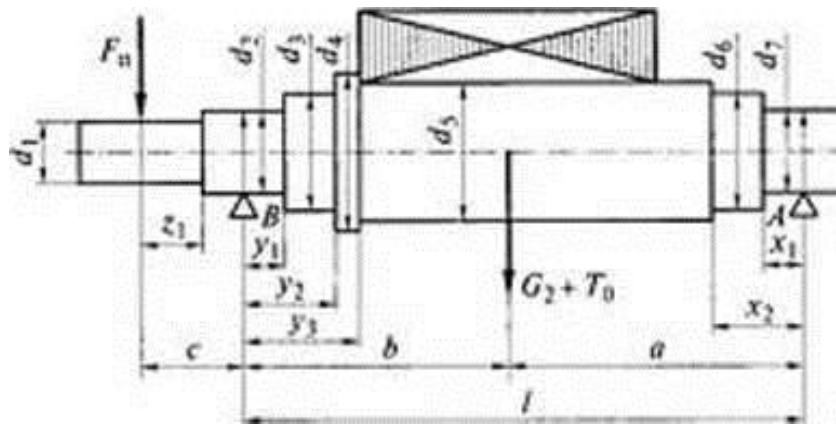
Ескіз до механічного розрахунку вала
